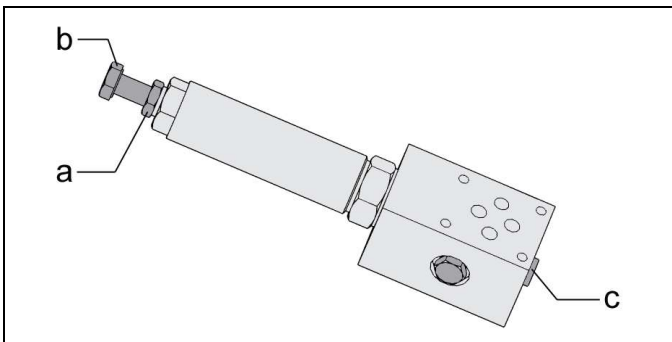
Válvula reguladora de presión de asiento (diseño de placas intermedias)
